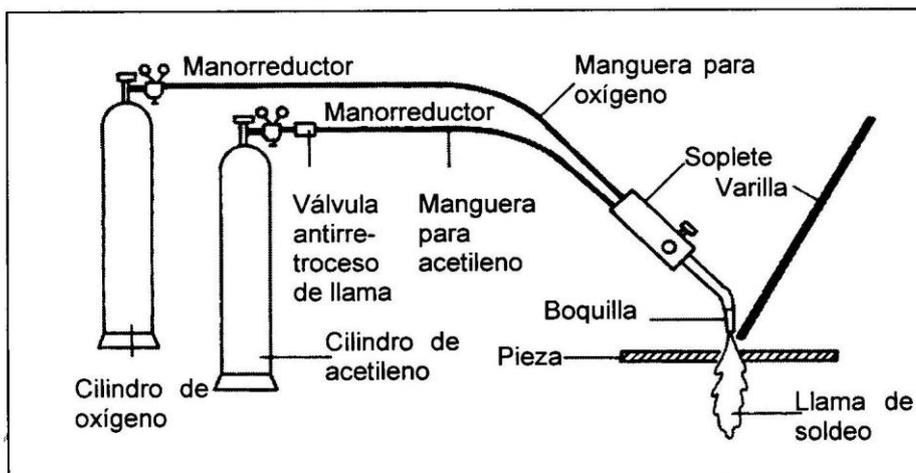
Instalación de soldeo oxi-acetilénico.
